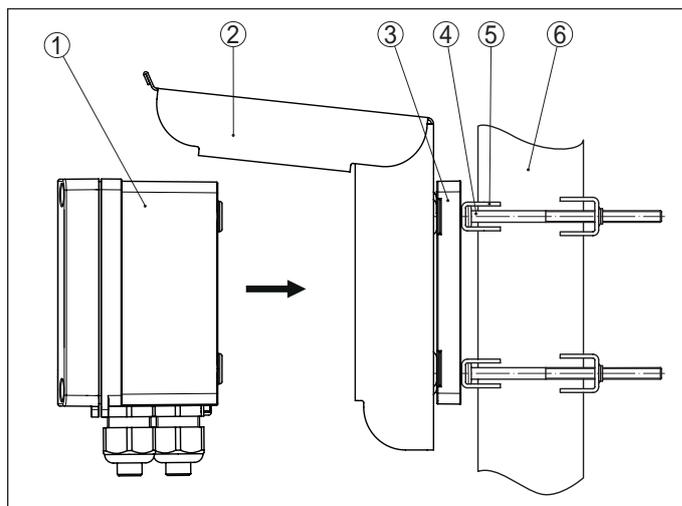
Montaggio della protezione dall'irradiazione solare in caso di montaggio su tubo
